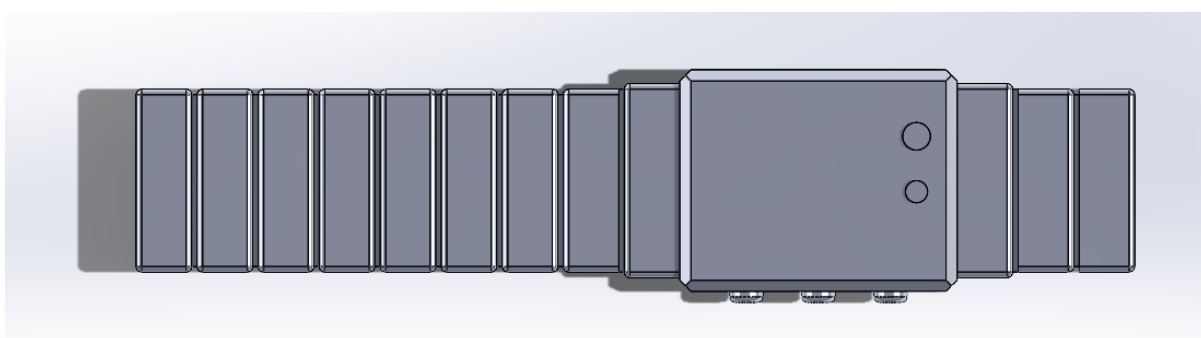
Diseño detallado, vista superior. Fuente: Elaboración propia.
